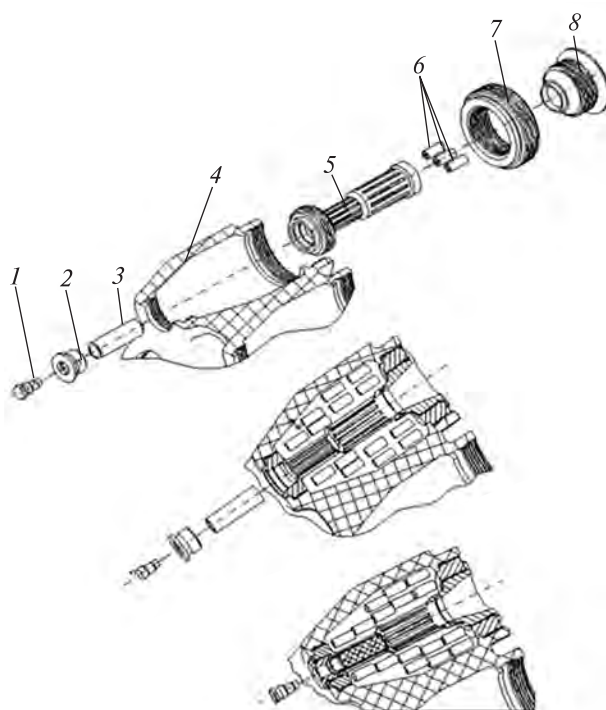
Схема сборки импульсных твердотопливных ракетных двигателей: 1 — пиропатрон, 2 — крышка, 3 — воспламенитель, 4 — корпус, 5 — трубка-диафрагма, 6 — заряд, 7 — гайка, 8 — сопло
